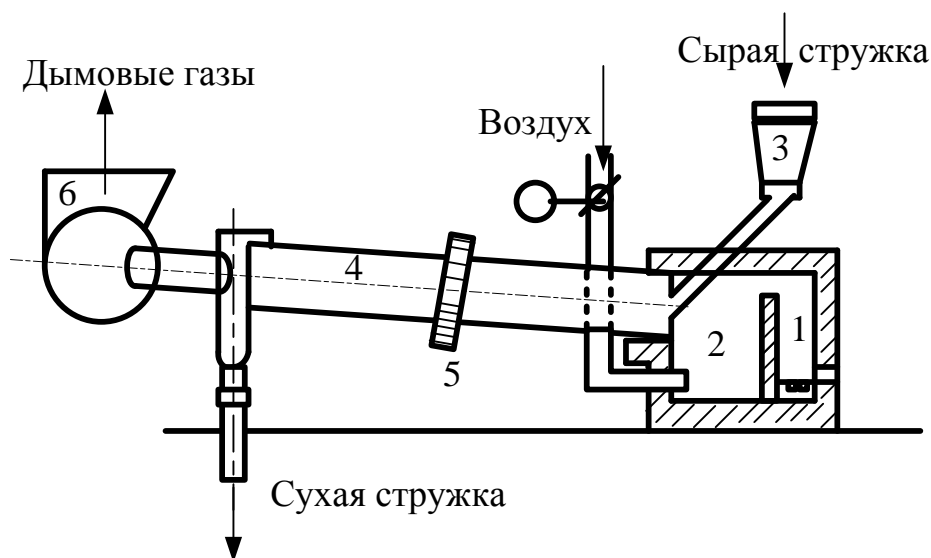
Барабанная сушилка для древесной стружки: 1 – топка; 2 – смеситель; 3 – загрузочное устройство; 4 – барабан; 5 – приводная шестерня; 6 – дымосос
